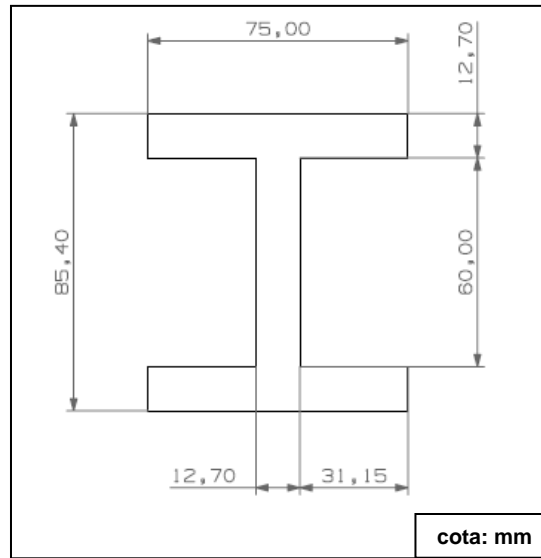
Sección transversal de las cuadernas 13 y 14.
